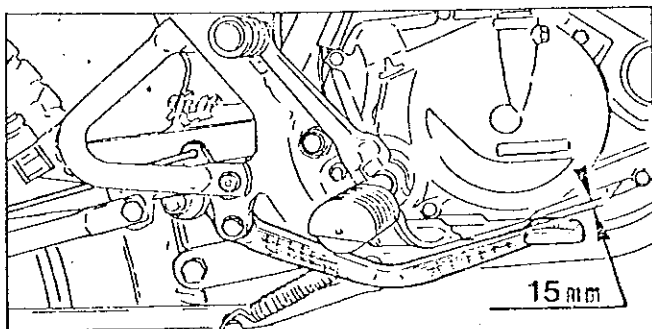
A - AJUSTE DO FREIO TRASEIRO
